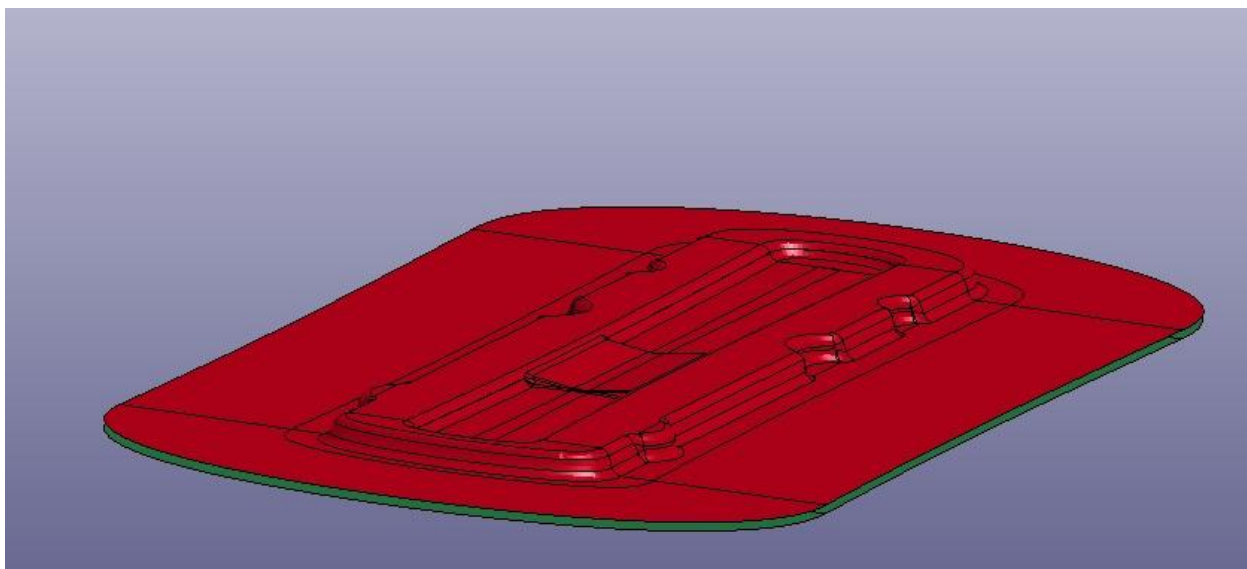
Ассоциативные копии поверхностей рабочего инструмента и заготовки
